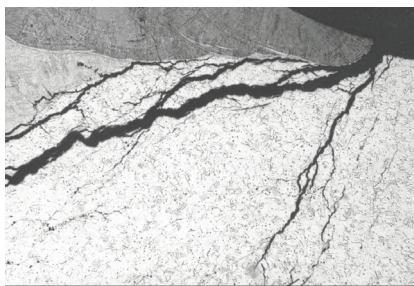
Agrietamiento por corrosión bajo tensión en soldadura en filete de acero inoxidable austenítico 316 y en zona afectada por el calor (Ref. 5).
